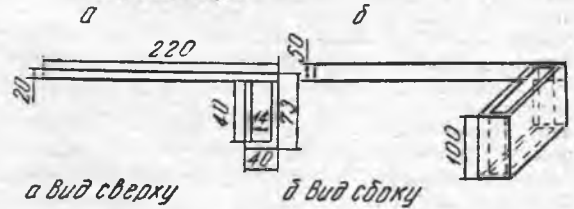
Детали дополнительного приспособления к ямокопателям типа ЯЮ-1, КПЯ-100 и БИГ-9.
